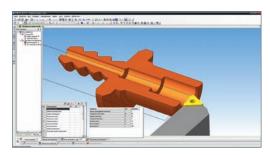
а, 7б, 7в. Выбор инструмента и приспособлений
